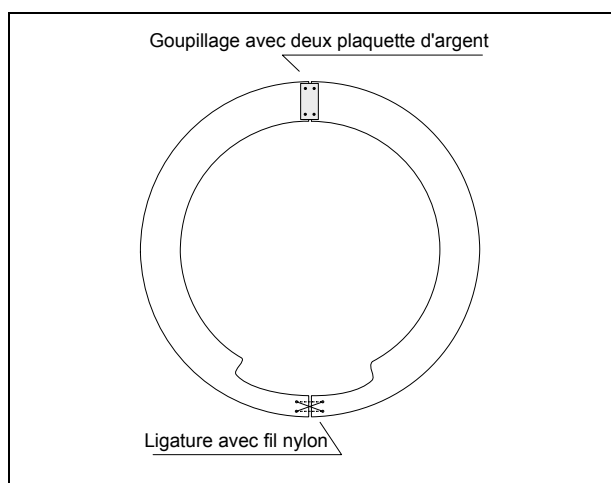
Schéma d'assemblage des anneaux en Plexiglas®.
